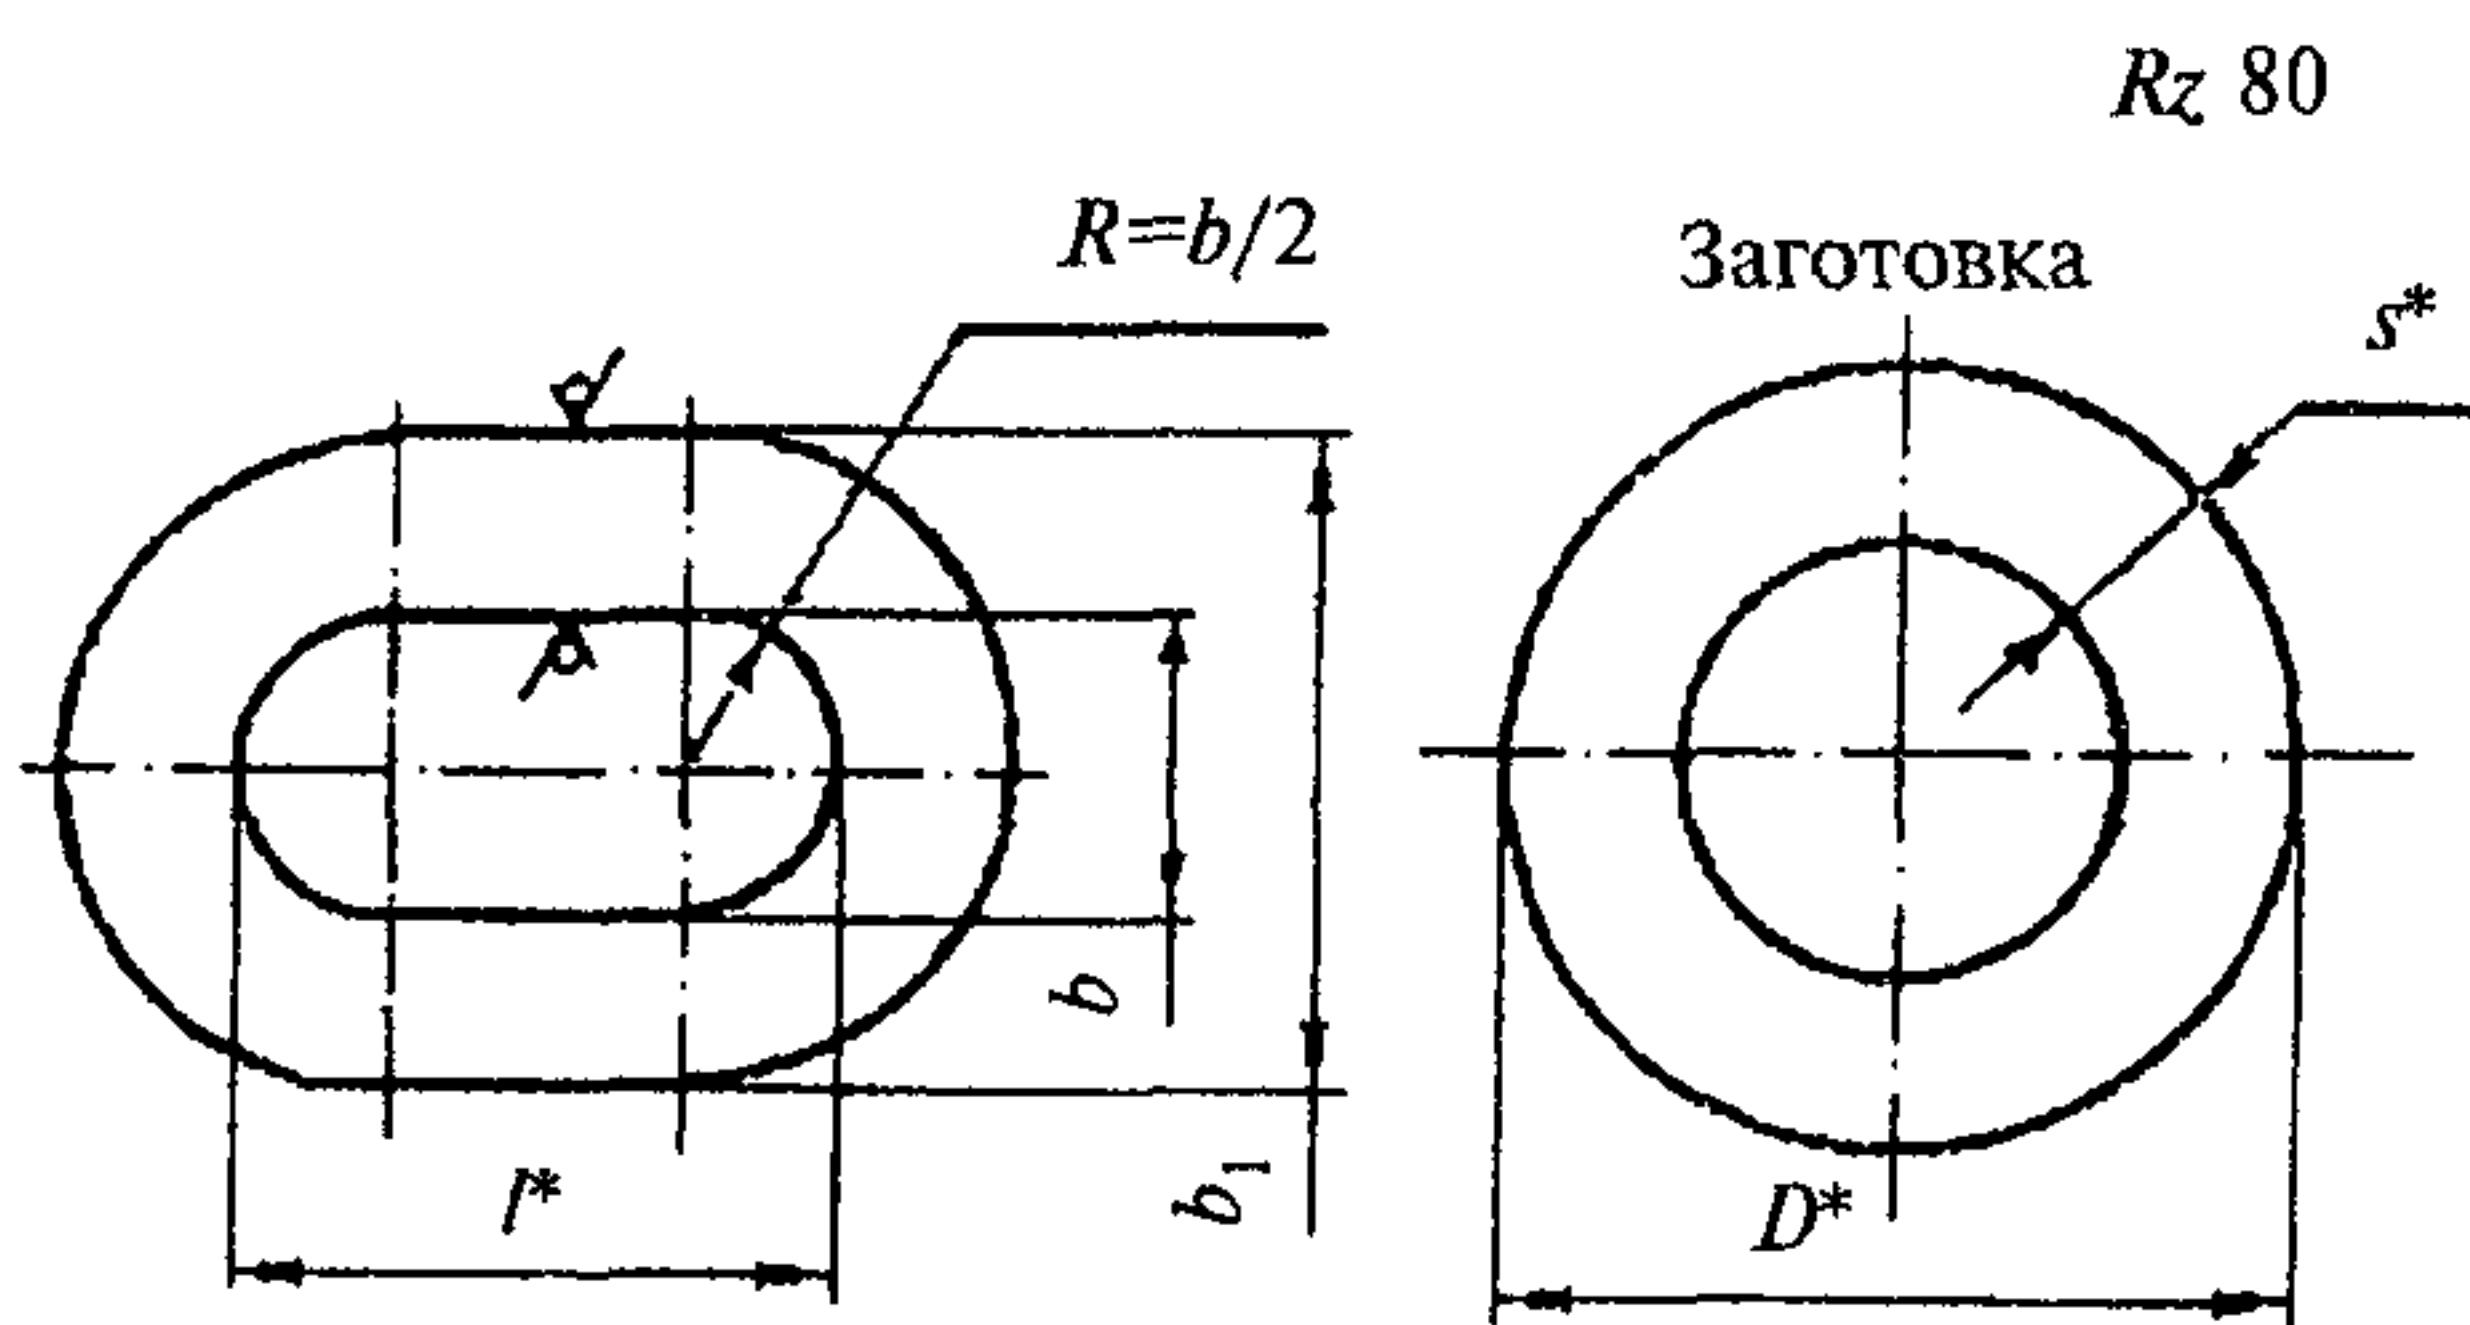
Заготовка алюминиевой втулки и алюминиевая втулка
